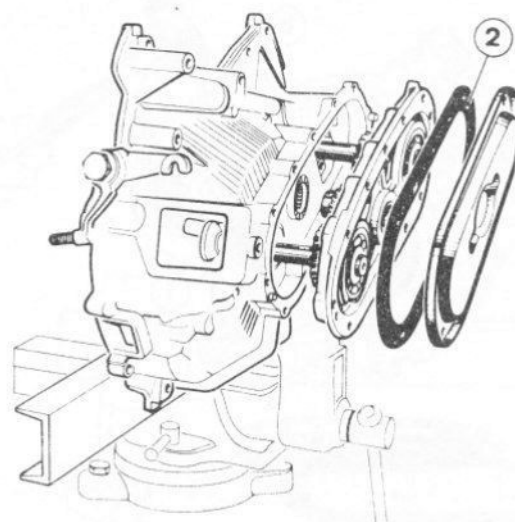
Assemblage de la pignonnerie de transfert et du couvercle (Sec 9)
